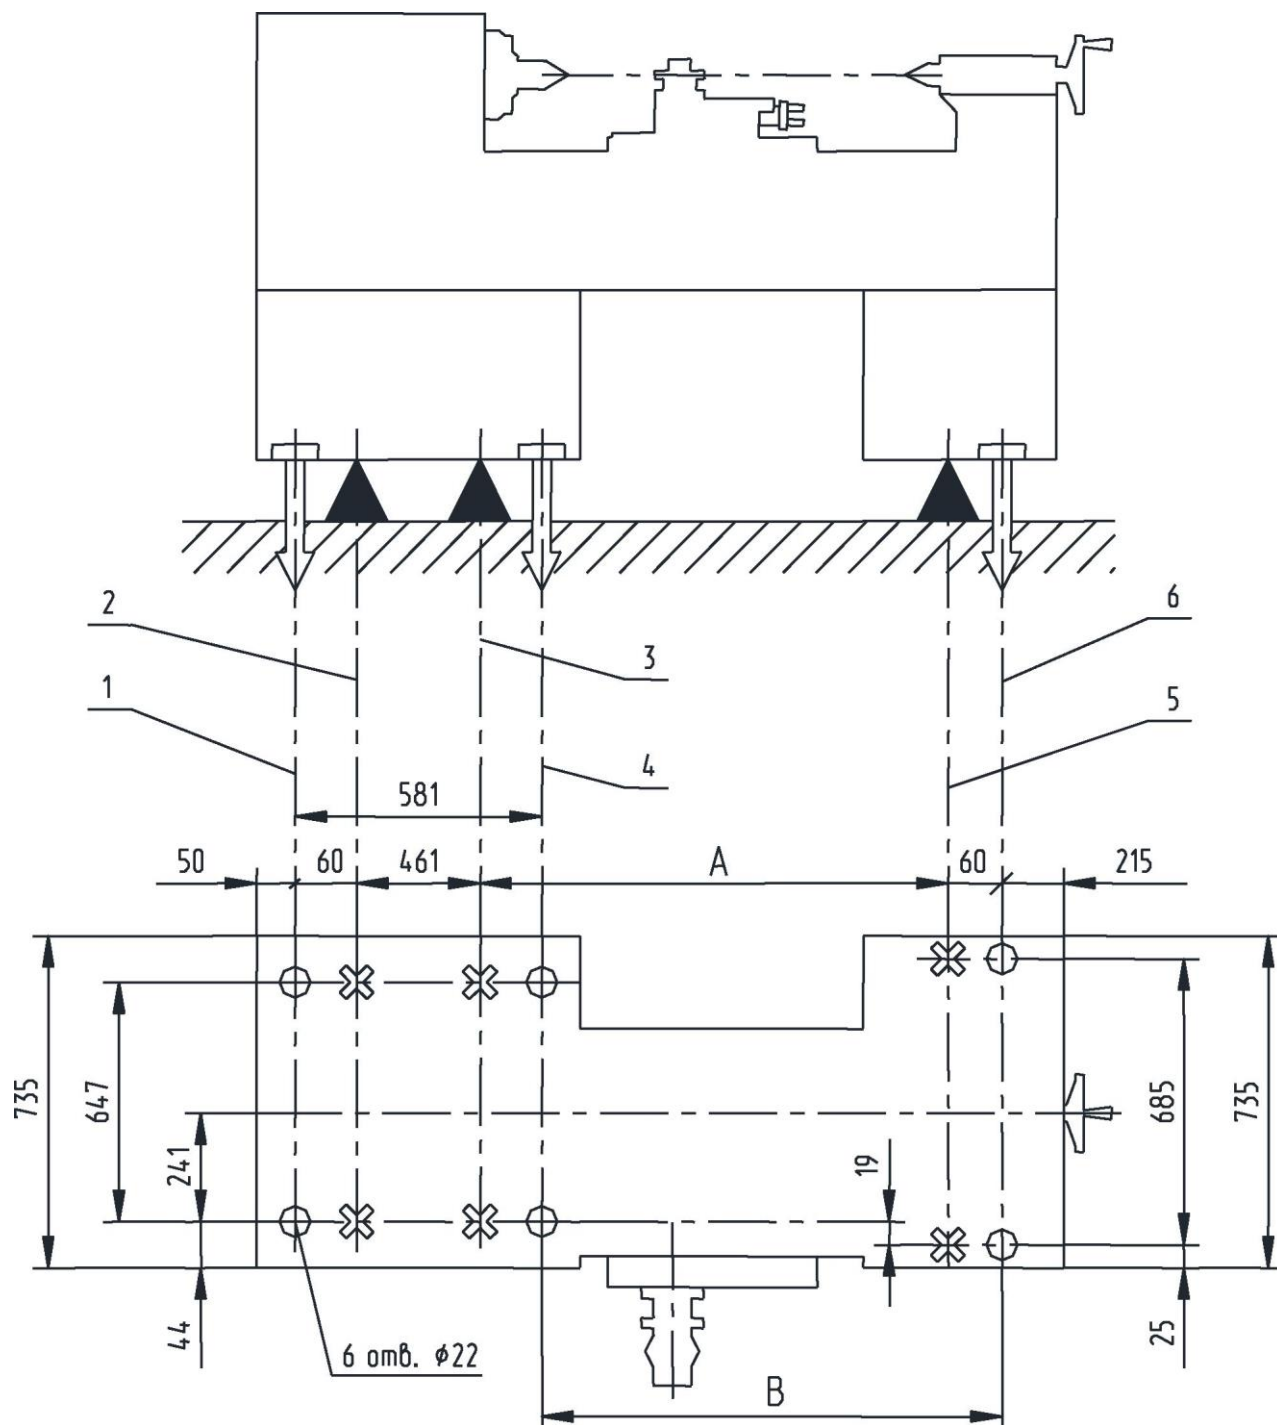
Установочный чертеж и схема подключения к электрической и пневматической сети станка с цельным основанием
